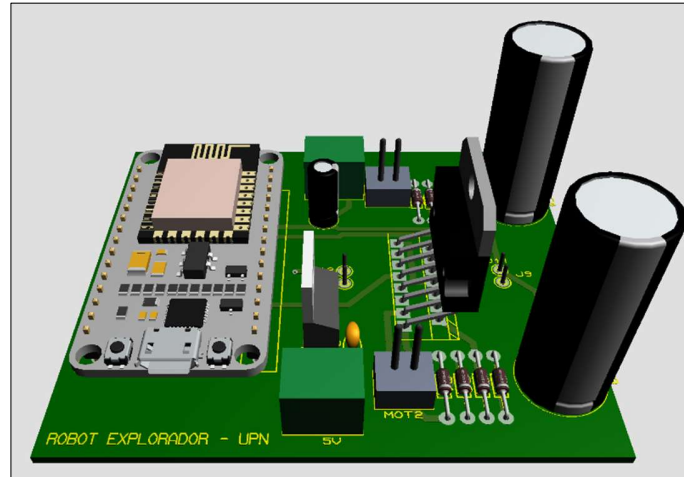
Vista final del PCB a fabricar en fibra de vidrio.
